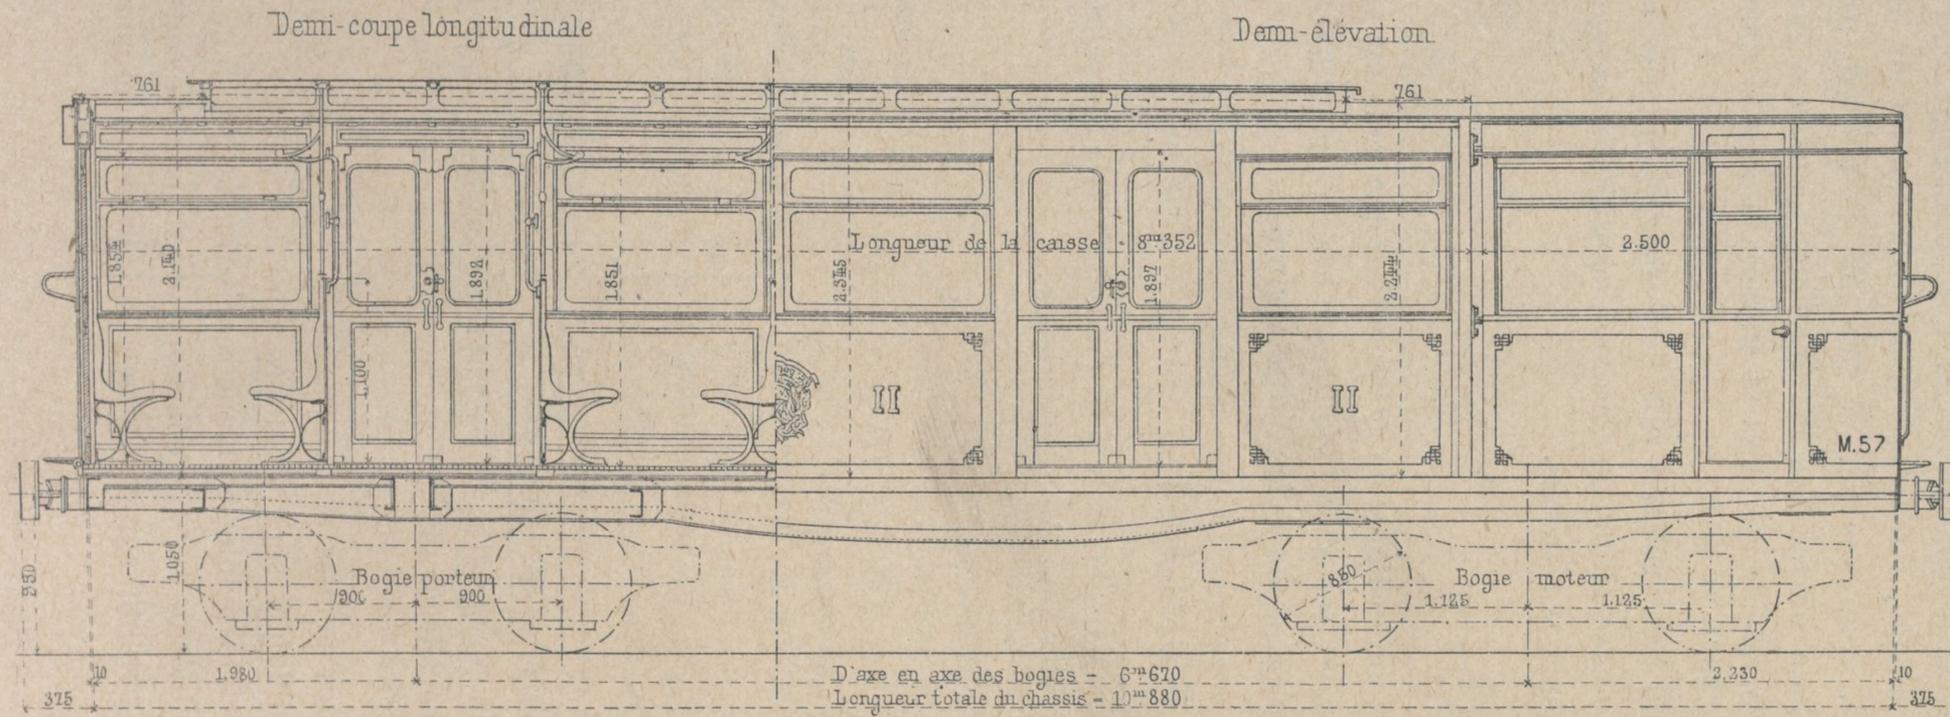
PLAN, ÉLÉVATION ET COUPE LONGITUDINALE DES VOITURES MOTRICES.
